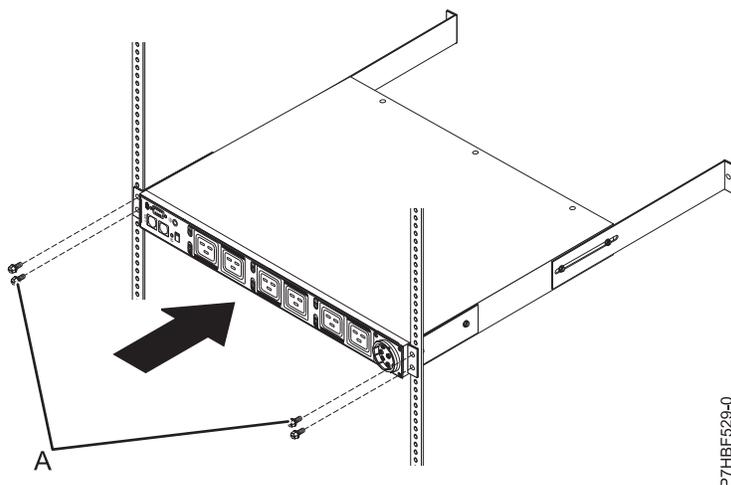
Conectando a frente da PDU+ ou da PDU alternada inteligente ao rack
